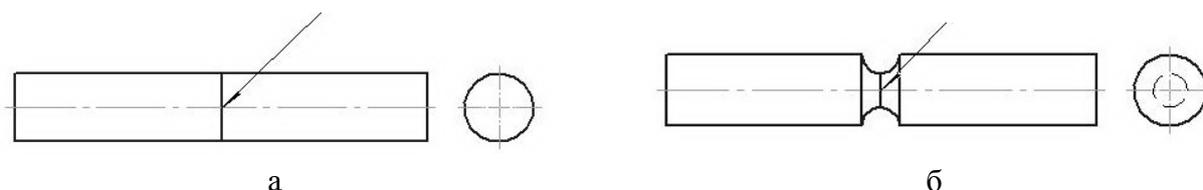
Форма цилиндрических образцов для испытания стыковых соединений по ГОСТ 6996-66:
